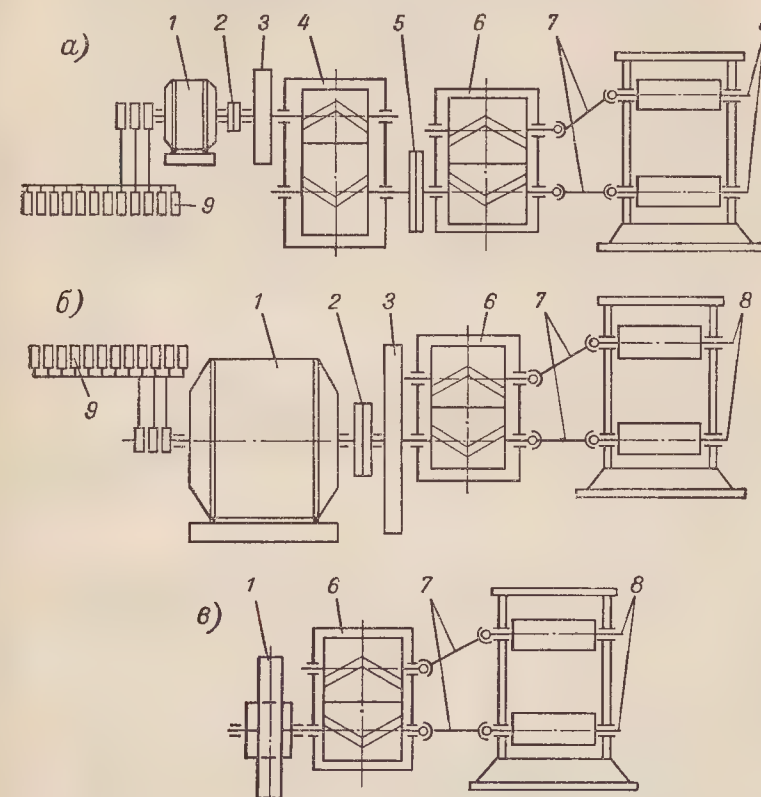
Варианты привода нерегулируемого прокатного стана: а — редукторный с малополюсным электродвигателем; б — безредукторный с многополюсным электродвигателем; в — безредукторный дугостаторный
